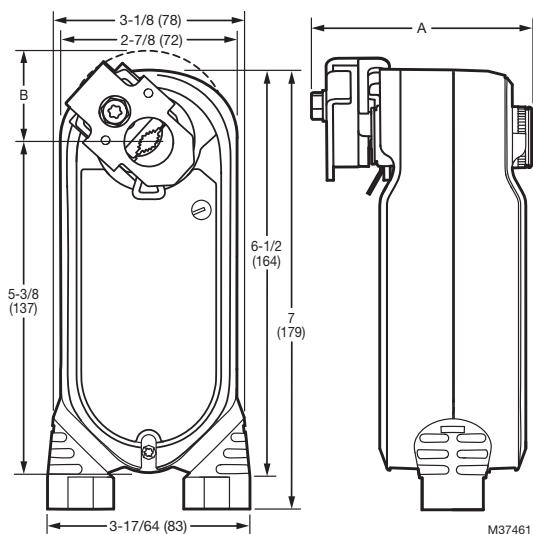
Габаритный чертеж исполнительного механизма в дюймах (мм). Размеры А и В см. в табл. 2.
